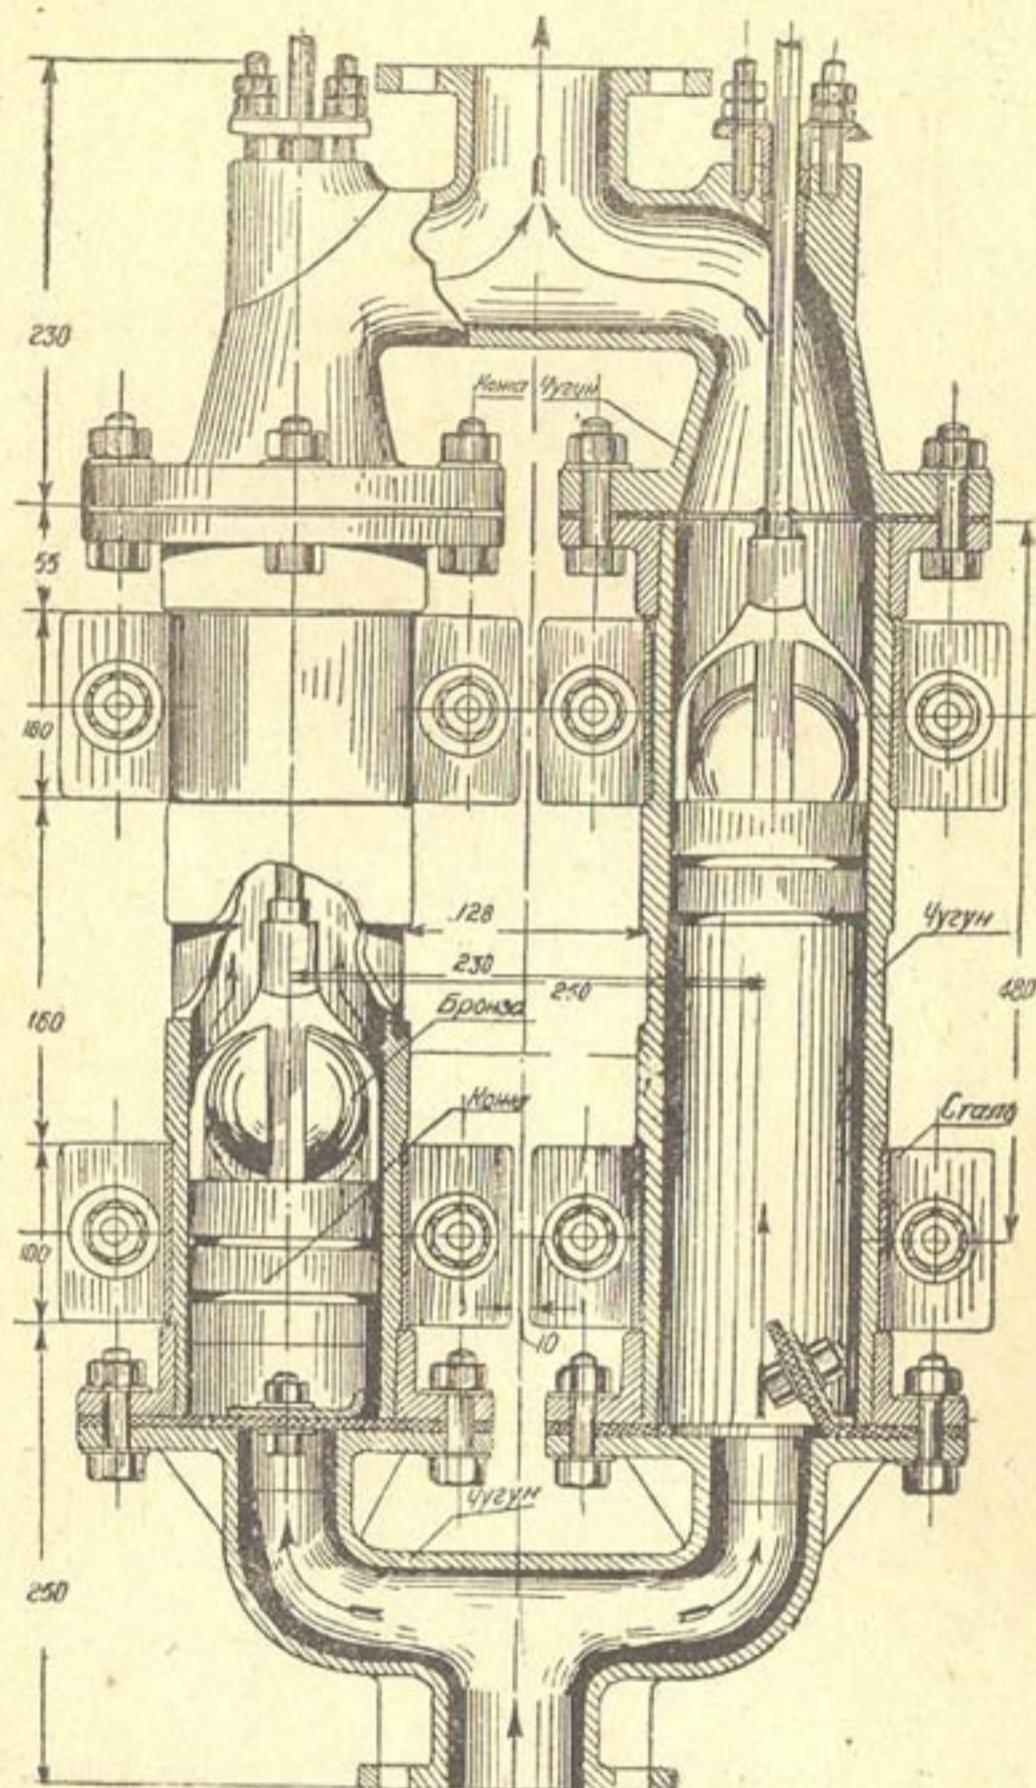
Сдвоенный штанговый поршневой насос типа А-2.
